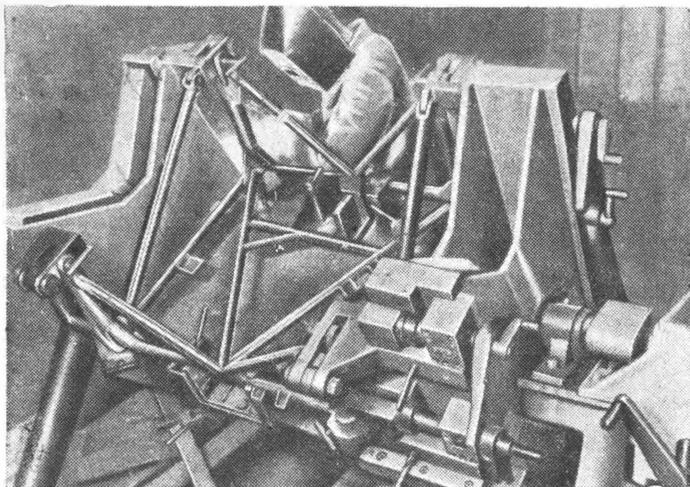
Приспособление для сборки и сварки моторамы.
